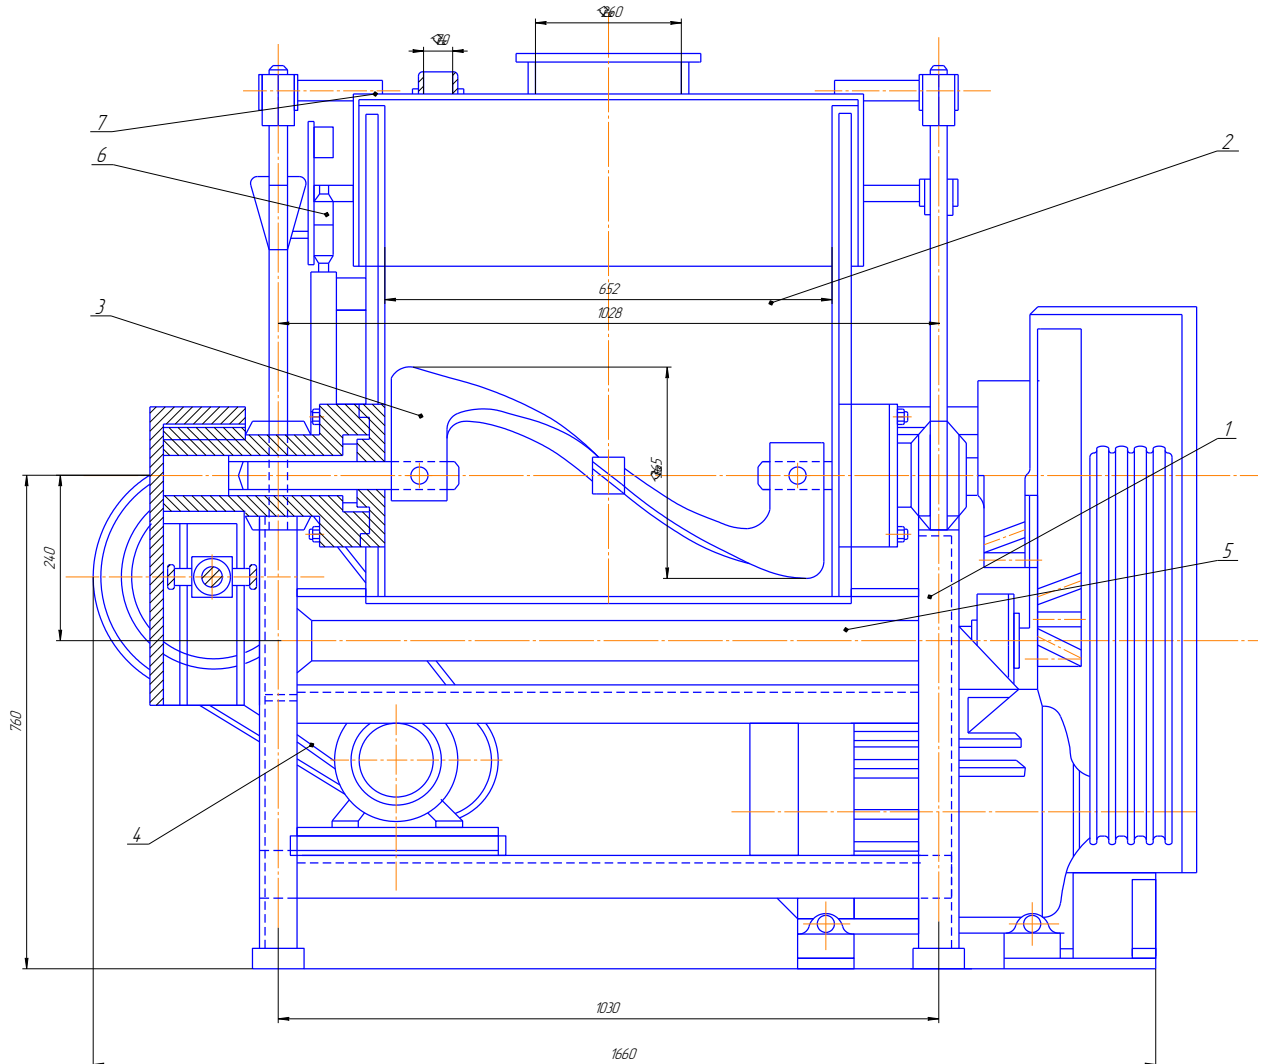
Загальний вигляд фаршесмішувача ФМ-6.
